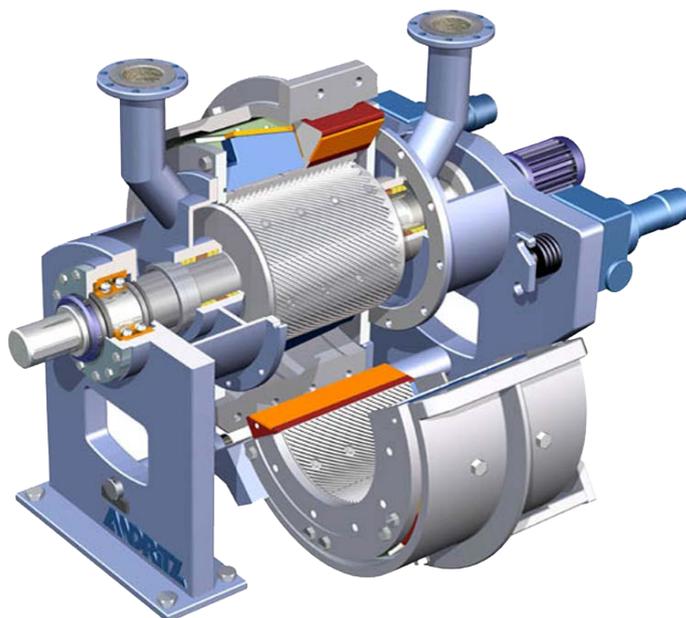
Внешний вид цилиндрического рафинёра Papillon
